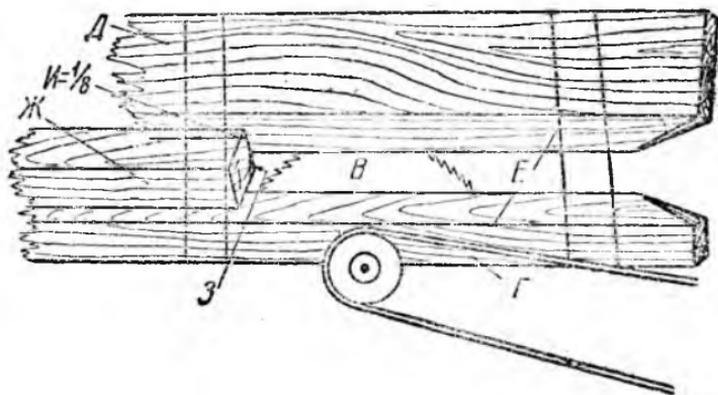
Схема приспособления к циркульной пиле для обрезки углов квадратных брусков
